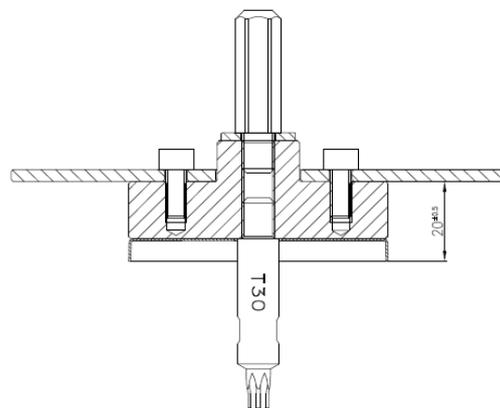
ejotherm STR U Montagewerkzeug Typ "S" für Dämmstoffdicken ab 80 mm
